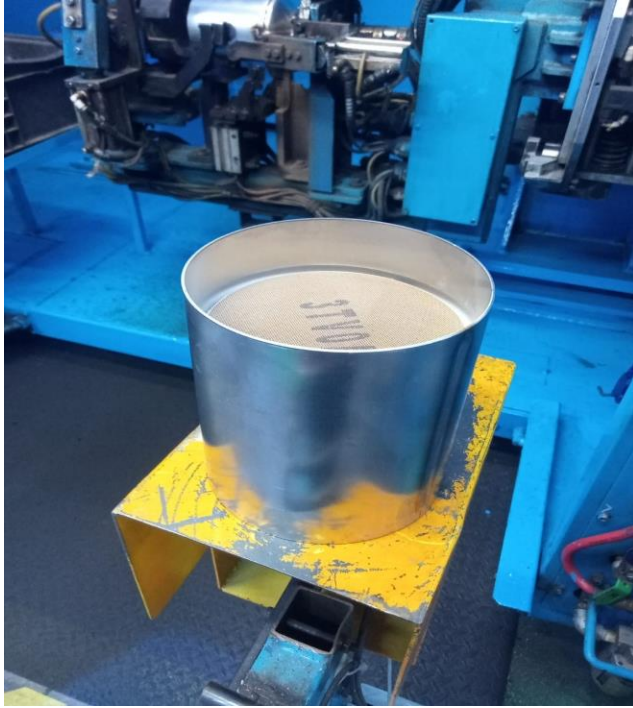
Imágenes referentes a la cabina #3 (lado B) de soldadura.
